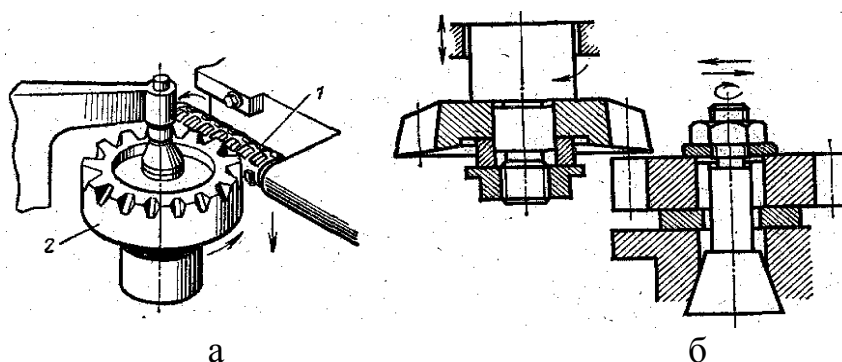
Нарезание зубчатых колес червячной фрезой и зуборезным долбяком
